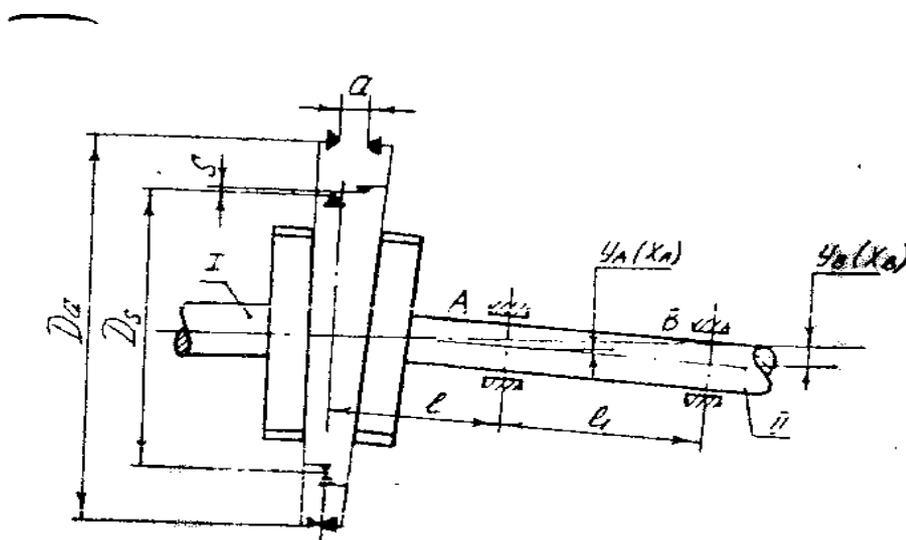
схема смещения опор вала для обеспечения центровки муфт
